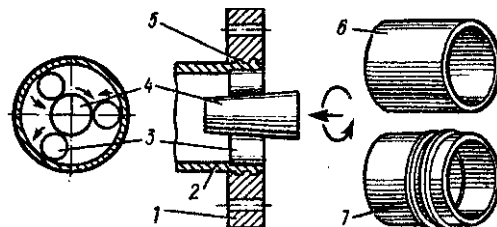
Схема вальцювання: 1 — фланець; 2 — кінець труби; 3, 4 — ролики; 5 — канавки; 6, 7 — труба до і після вальцювання
